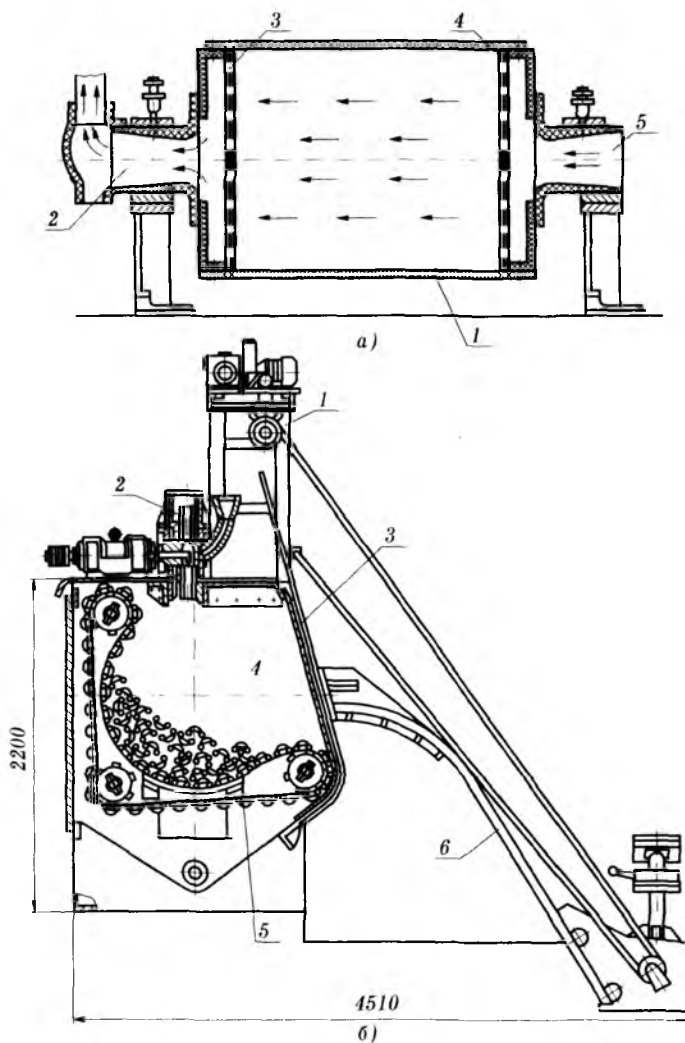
Схемы очистного (галтовочного) и дробе­мётного барабанов:
